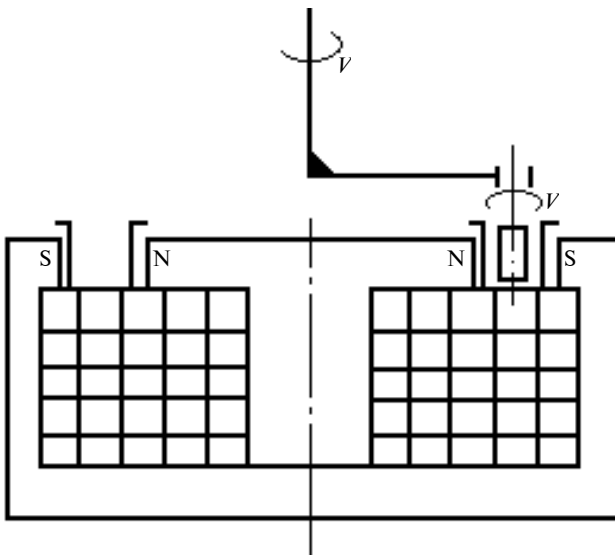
Принципова схема установки для магнітно-абразивної обробки
